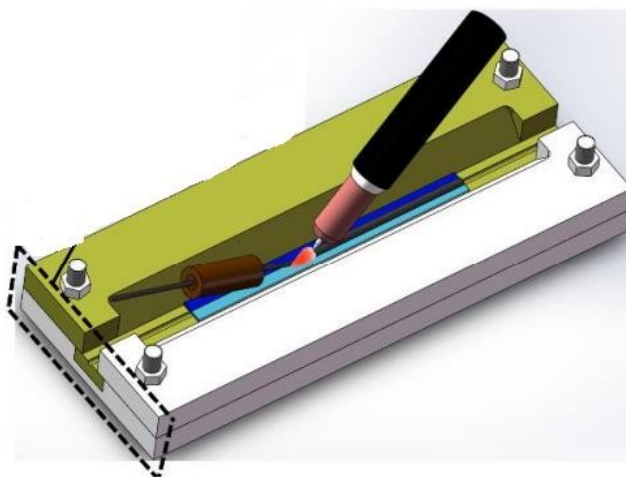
Принципиальная схема процесса сварки в условиях стационарного охлаждения
